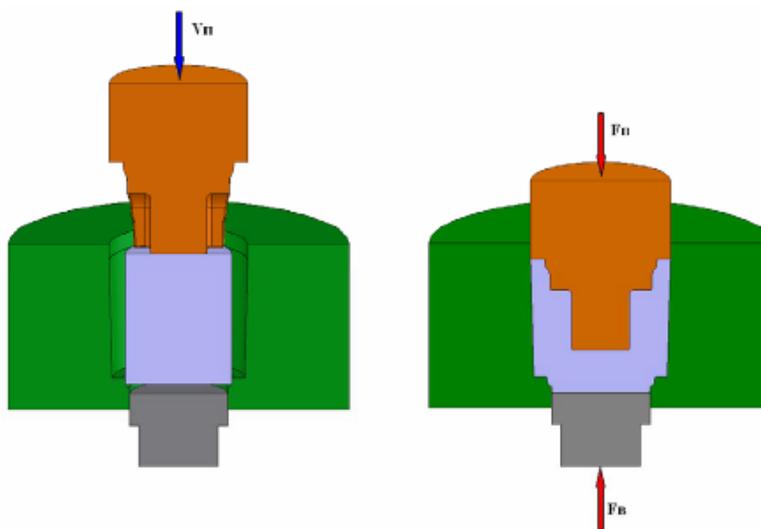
Схема тиксоформования заготовки поршня ДВС
